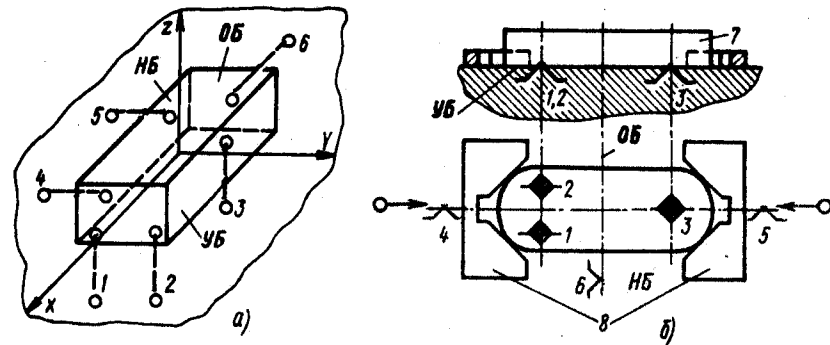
Схема базирования (а) и установки (б) заготовки на шесть опорных точек: 1–6 – двусторонние связи по опорным точкам, 7 – заготовка, 8 – губки тисков; УБ – установочная база, НБ – направляющая база, ОБ – опорная база
